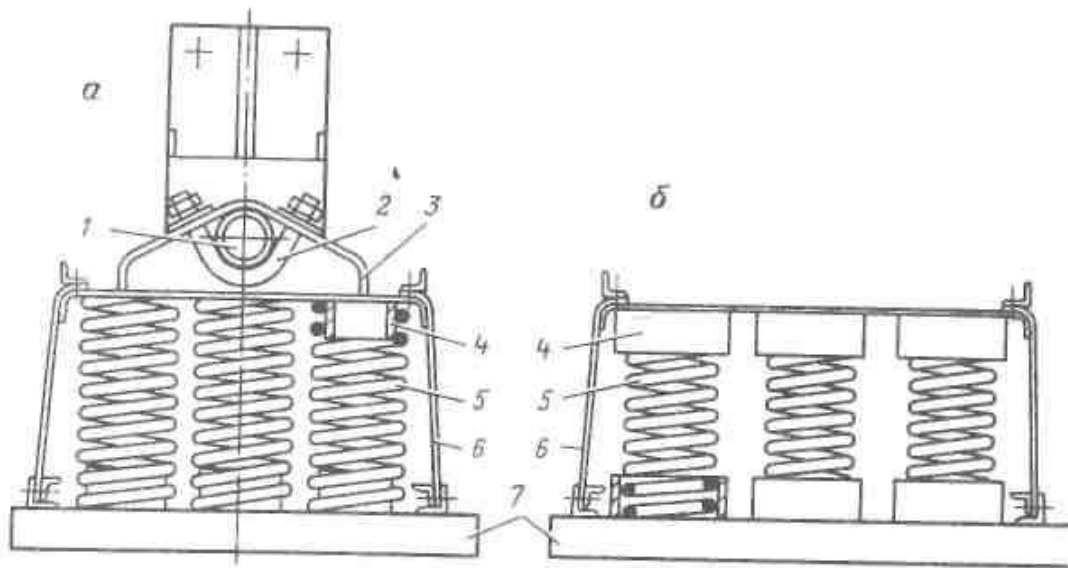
Пружинна віброізоляційна опора грохоту ГІС-72
